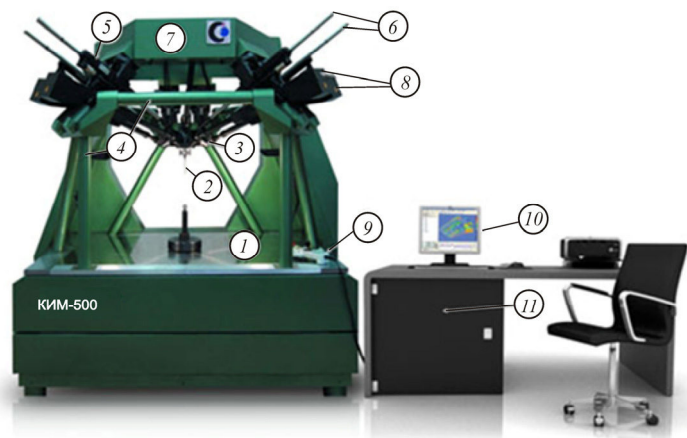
Схема конструкции КИМ-500: 1 – стол; 2 – инструмент (измерительный щуп или шпindelь); 3 – каретка с 6 шарнирами; 4 – измерительная рама; 5 – электроприводы, 6 шт.; 6 – стержни переменной длины (ШВП, 6 шт.); 7 – силовая рама; 8 – лазерные интерферометры, 6 шт.; 9 – пульт управления; 10 – ЭВМ оператора; 11 – промышленная ЭВМ, встроенная в стол оператора
